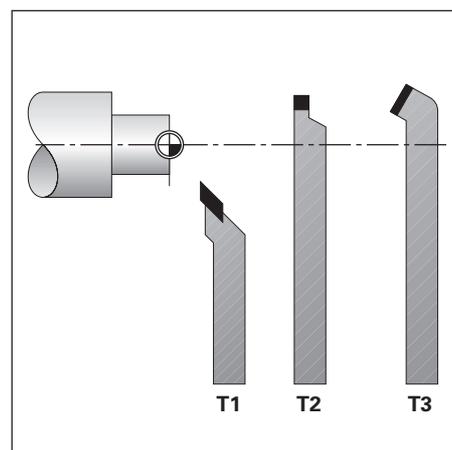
Las herramientas representadas tienen diferentes dimensiones
